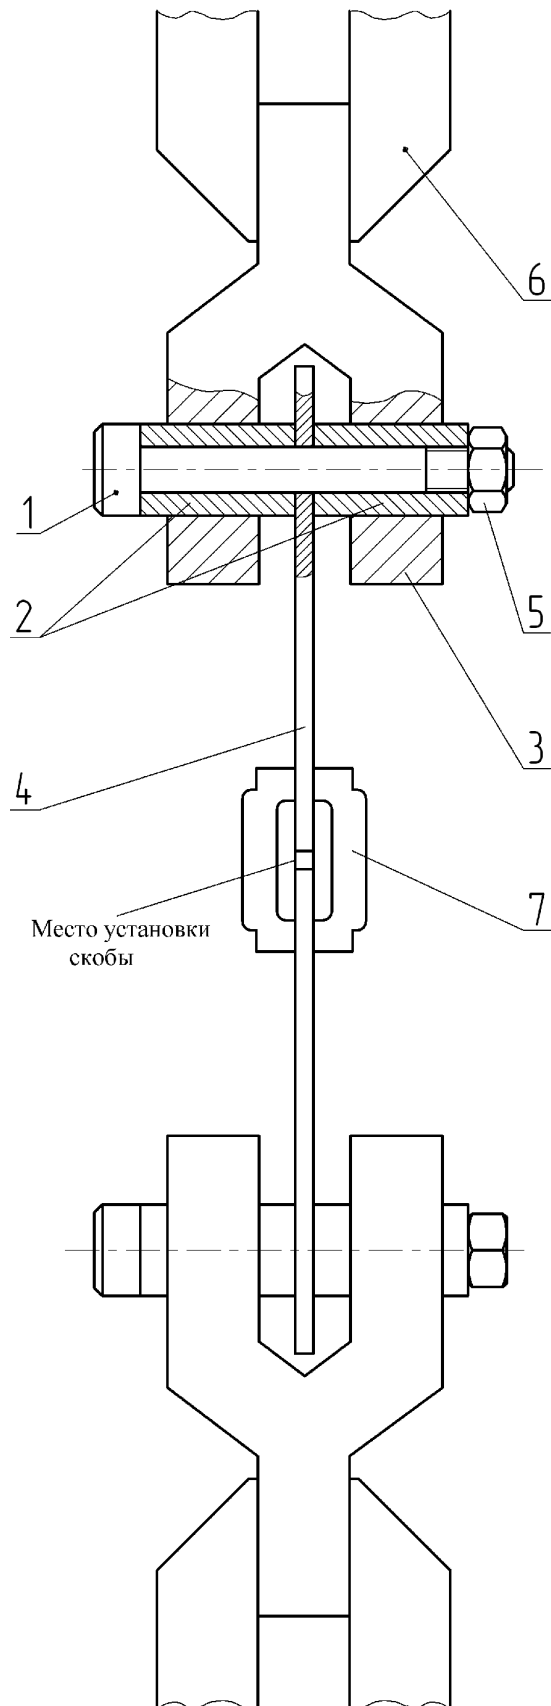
Схема приспособления для установки образцов малой толщины: 1) болт; 2) втулка; 3) вилка; 4) образец; 5) гайка; 6) захваты; 7) магнит
